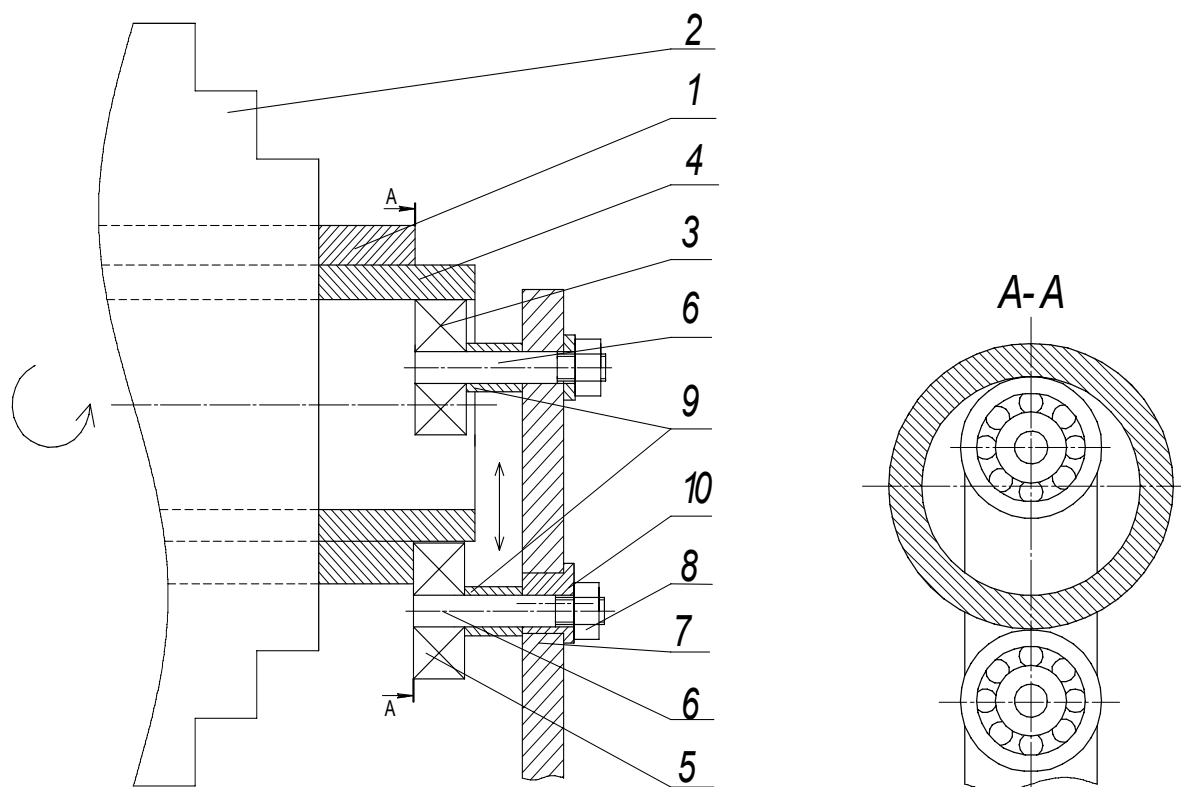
Устройство для отрезки трубчатых заготовок от цилиндрической трубы
